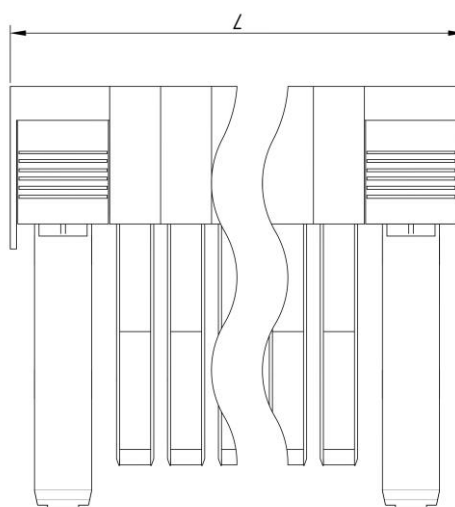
Общий вид рабочей крышки ЭПК. Вид сверху.
